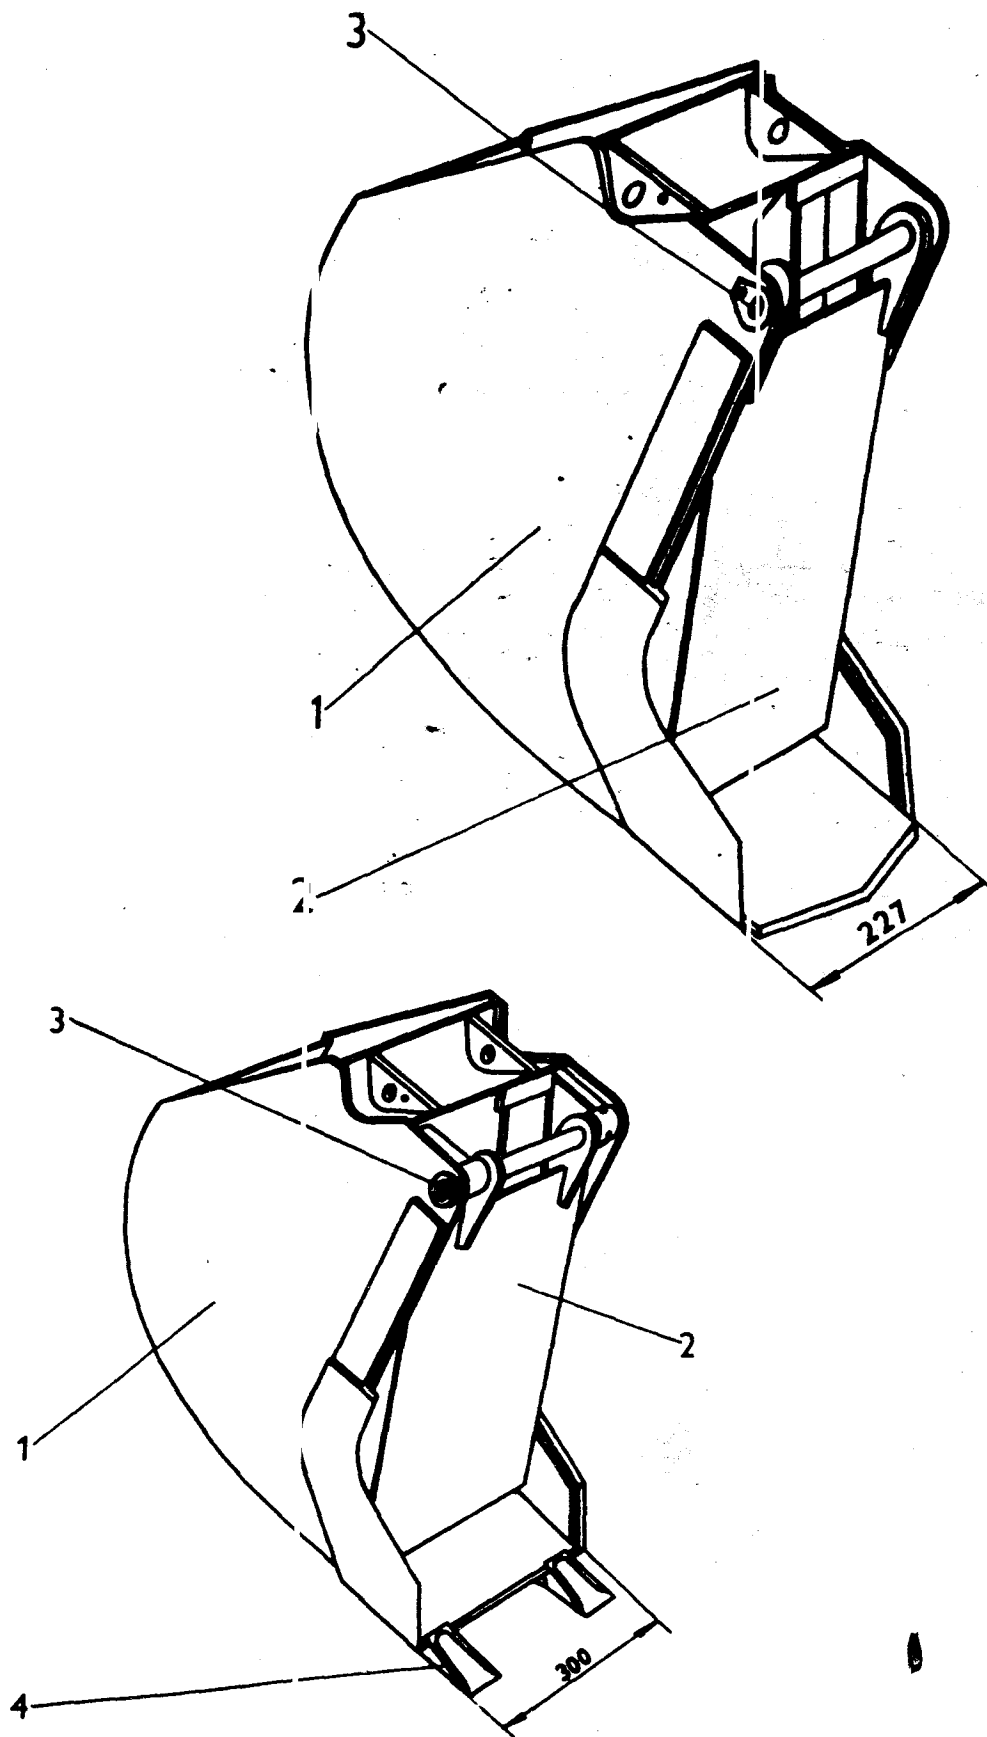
Дренажный ковш. 1 - ковш, 2 - выталкивающее днище, 3 - палец ковша, 4 - зубья
